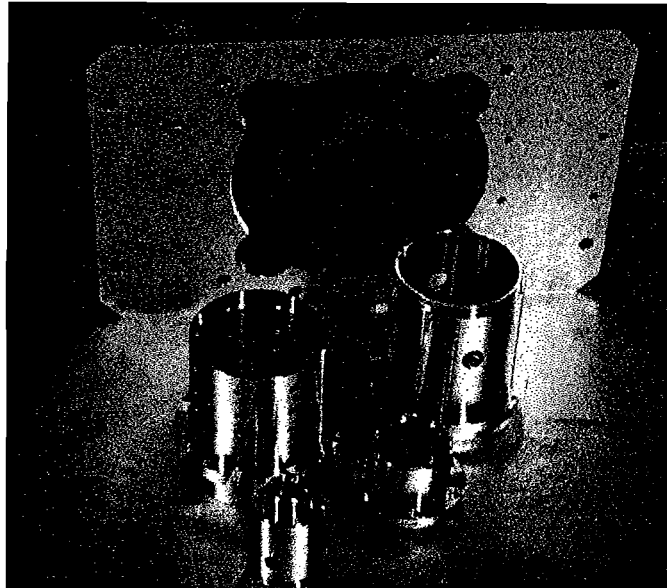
Photo des tubes rectifiés utilisés pour l'assemblage des lentilles. En arrière plan, on voit la plaque sur laquelle sera posé l'ensemble.
